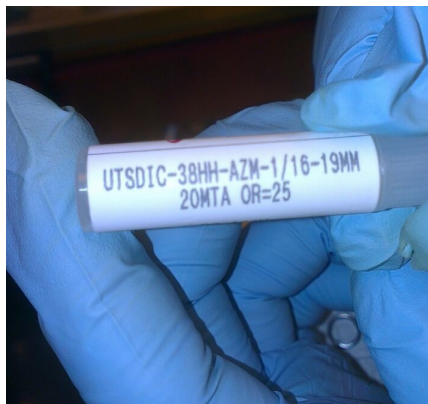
Envase de la boquilla usada en la alambreadora del CNMN.
